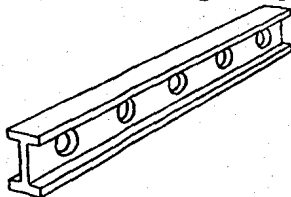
Regla de acero de planitud con caras planas y paralelas
